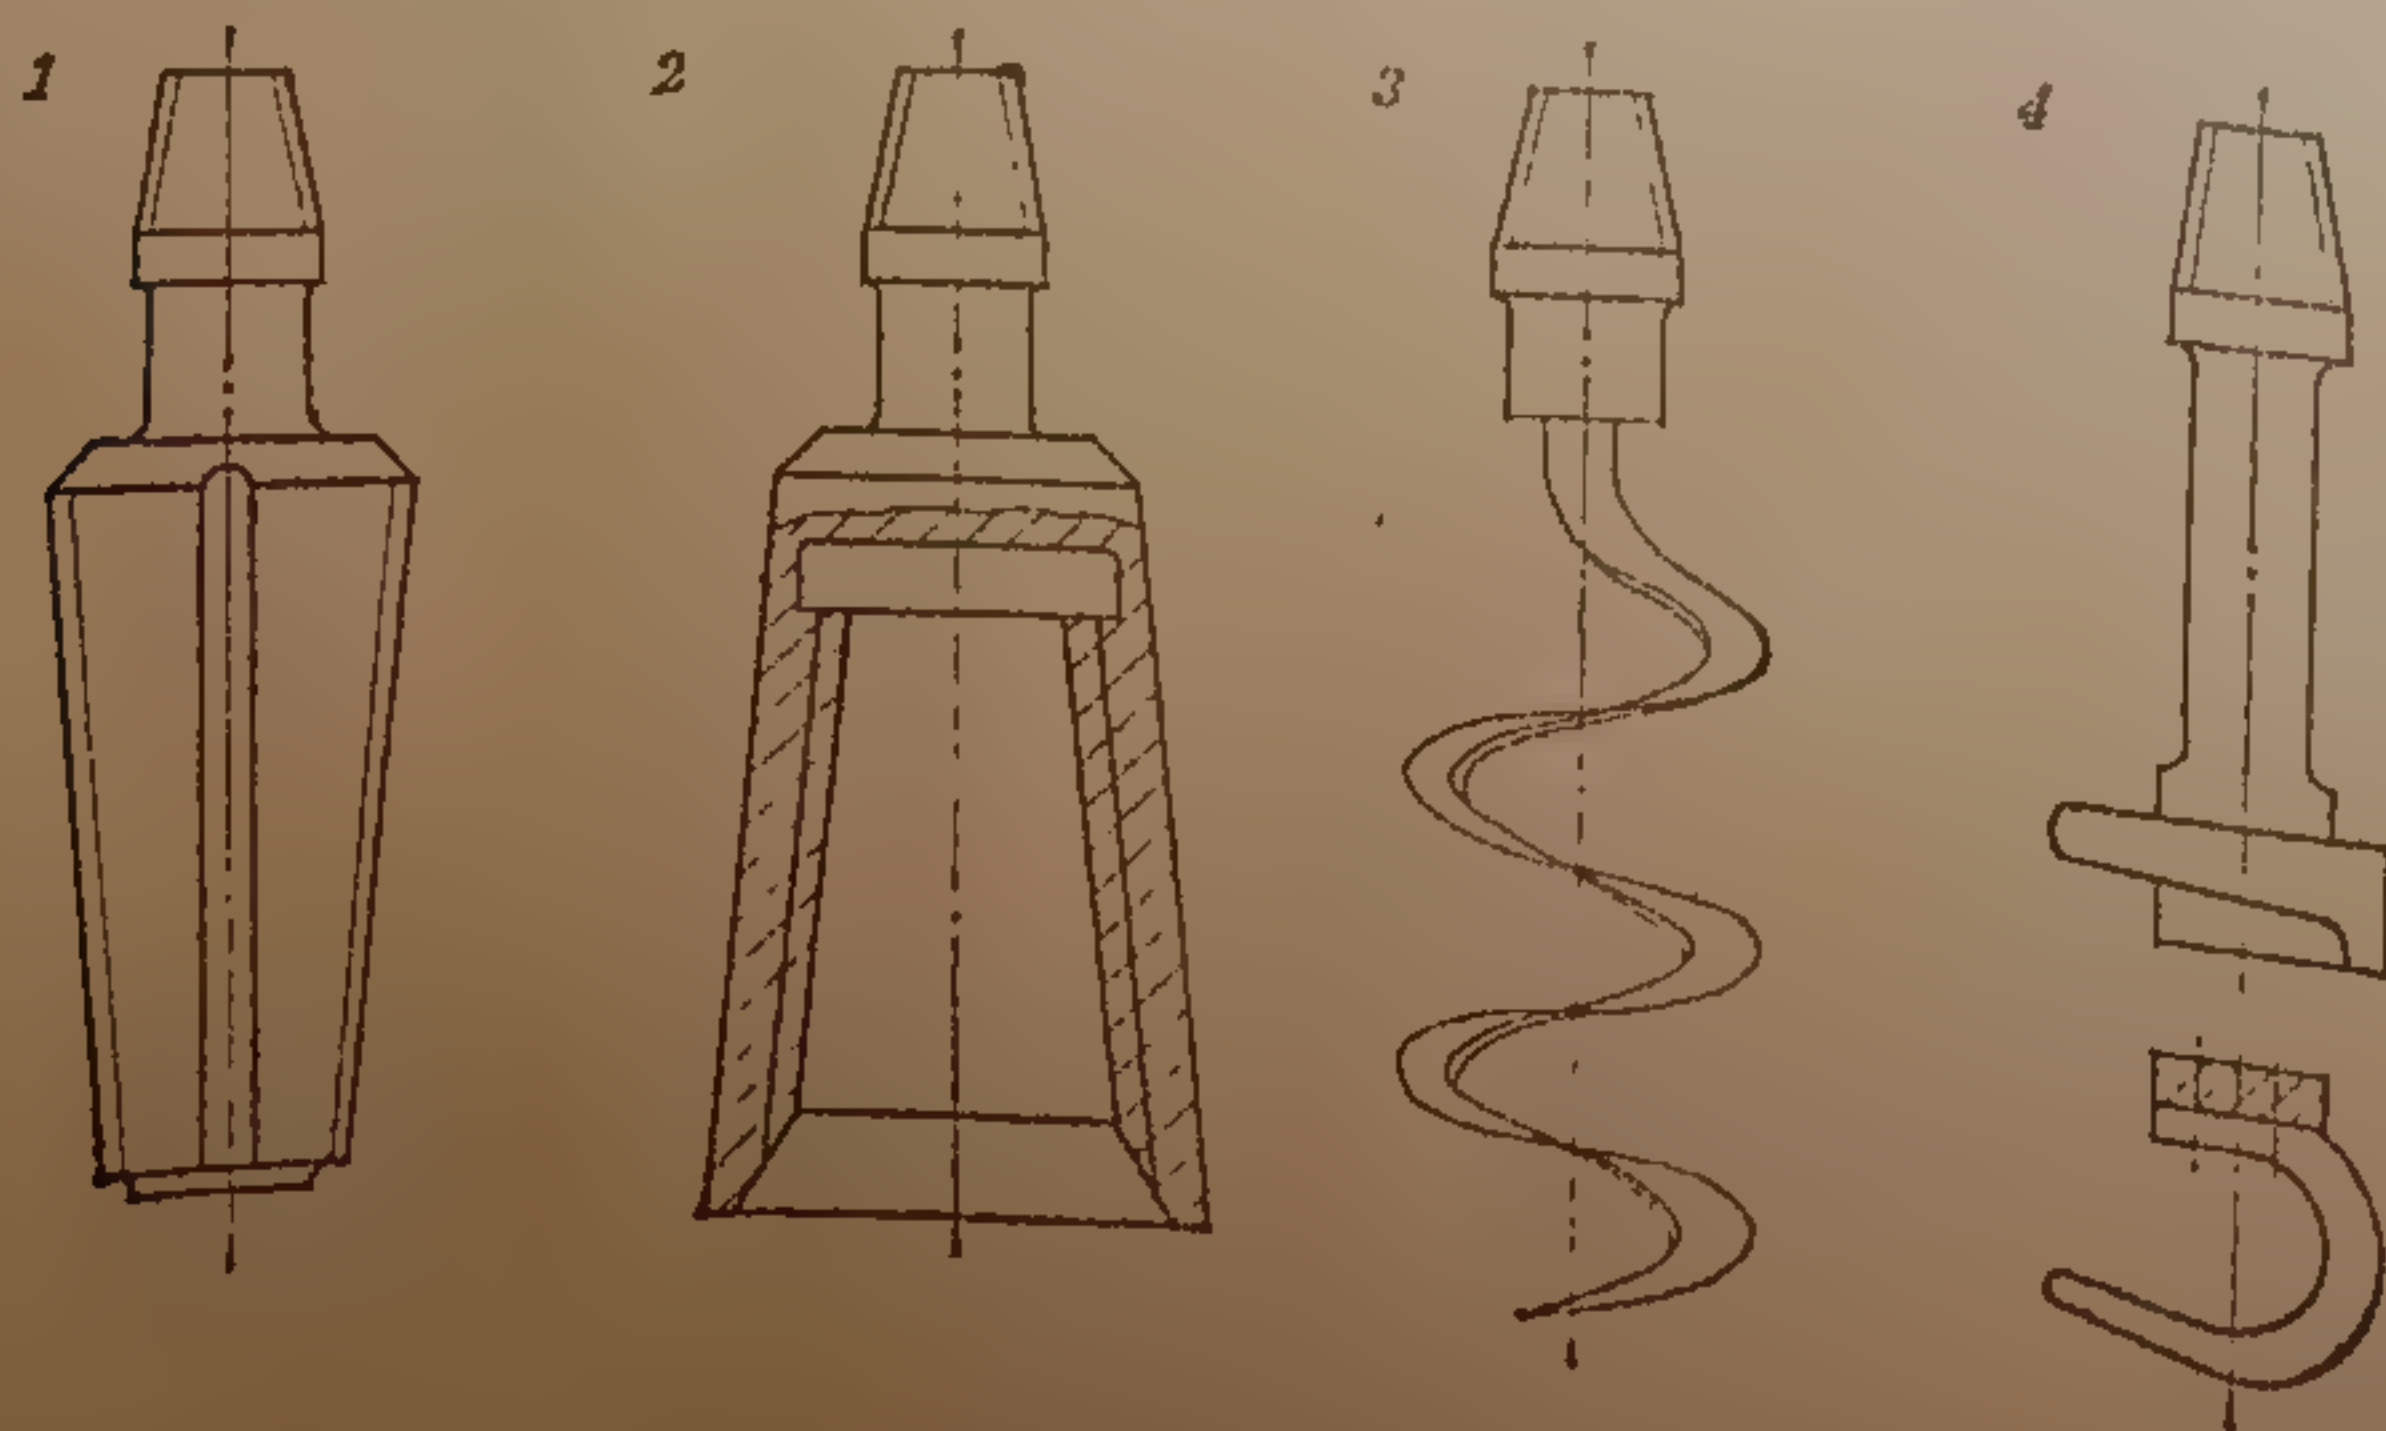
Ловильный инструмент: 1 — винт (метчик); 2 — колокол; 3 — штопор; 4 — «счастливый» крюк
